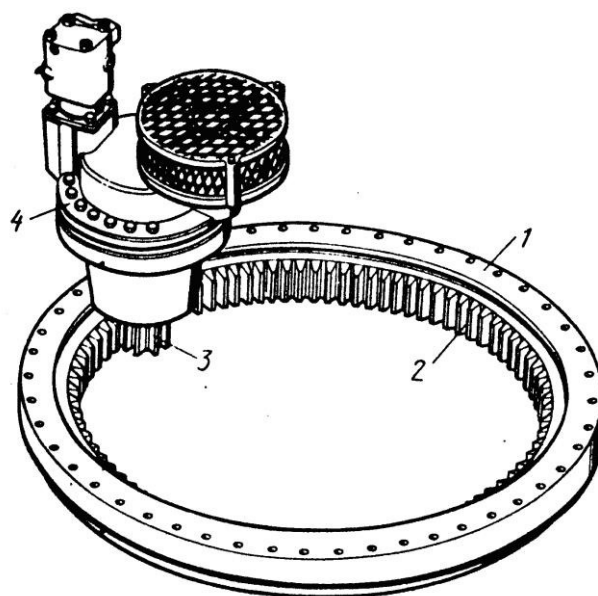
Опорно-поворотний пристрій і привод: 1 - зовнішнє кільце; 2 - внутрішнє (зубчасте) кільце; 3 - шестірня; 4 - редуктор
